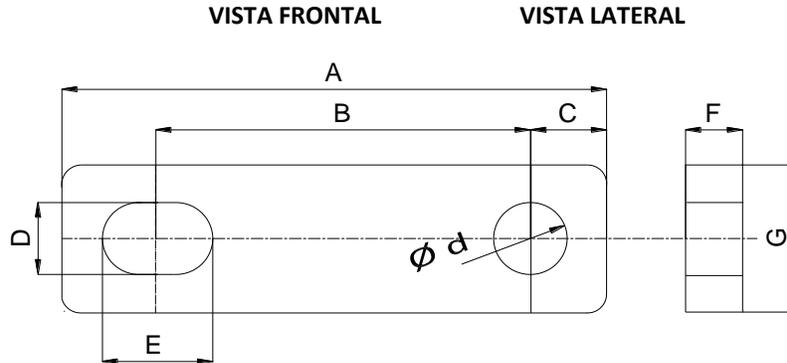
a: Herrajes para cruceta - Detalles de planchuela
